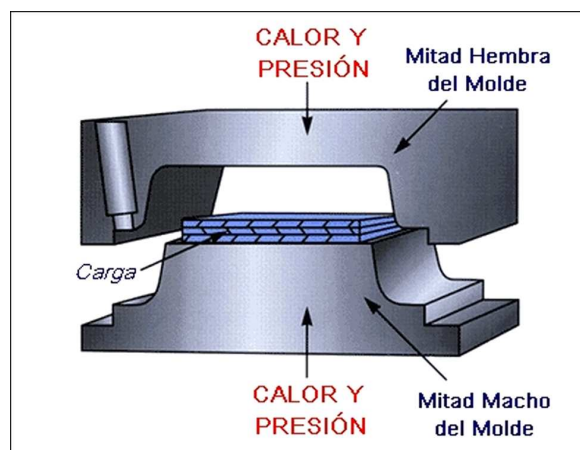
Molde tipo hembra-macho para moldeo por compresión.
